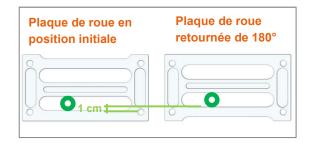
Modification de la hauteur d'assise à l'arrière en retournant la plaque de roue de 180°
